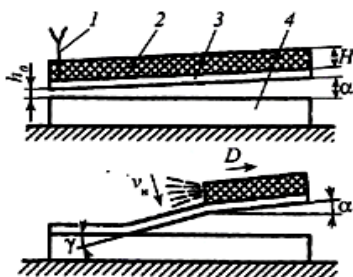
Схема сварки взрывом: 1-детонатор, 2- взрывчатое вещество, 3и 4 - заготовки
